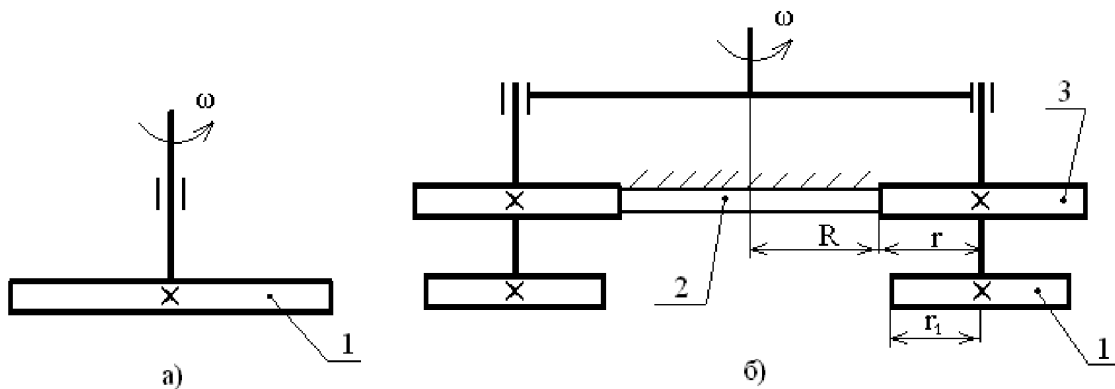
Дискový рабочий орган: а) с простым вращением; б) с планетарным движением; 1 — заглаживающий диск; 2 — неподвижное колесо; 3 — обкатывающееся колесо
